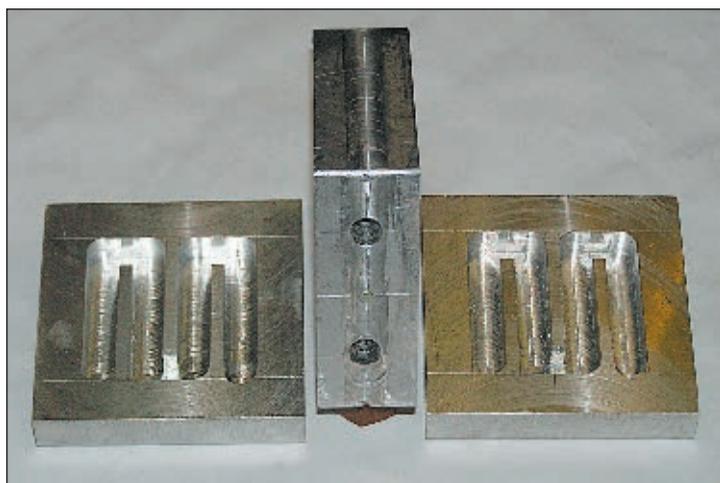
Внешний вид заготовок и теплообменника (в центре), сваренного стыковыми швами
